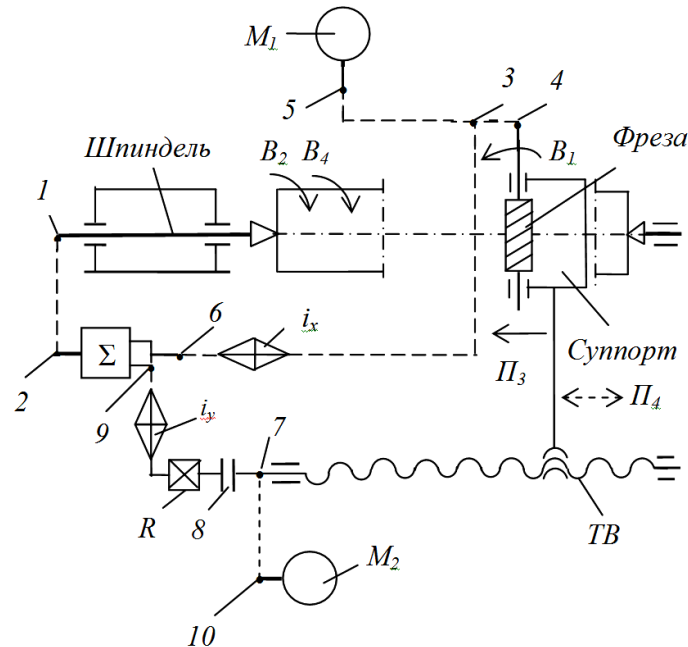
Структурная схема шлице-зубофрезерного станка с отдельными регулируемыми приводами
